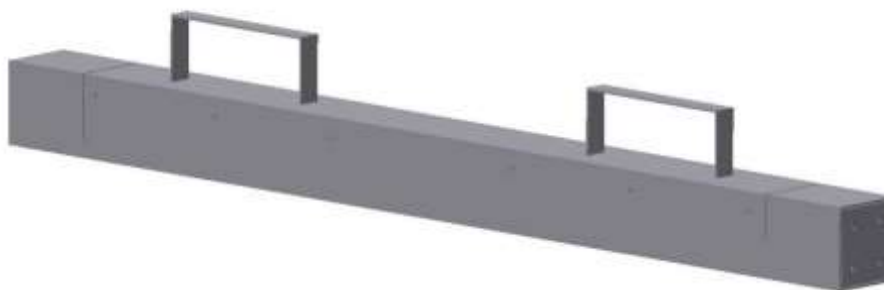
Pneumatický manipulátor – pohled 2 [7]
